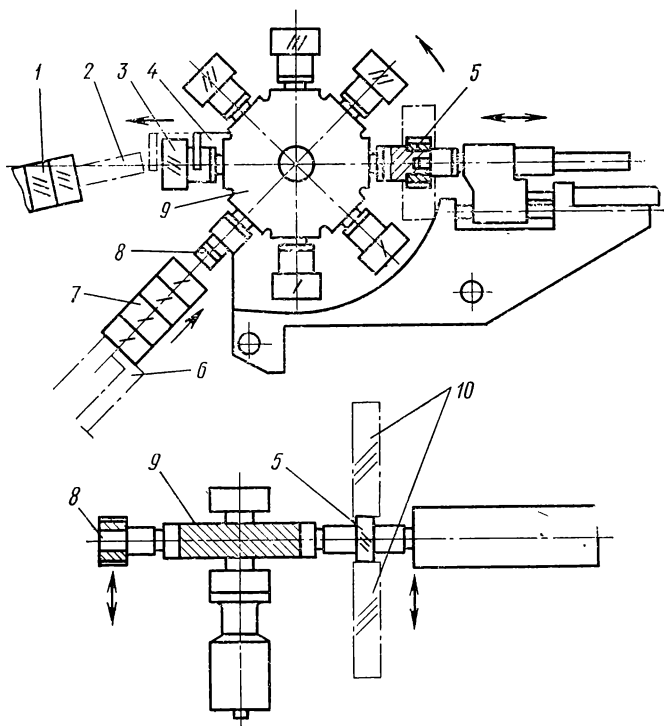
Схема работы двухшпindelного прикатного автомата с двумя накатниками
